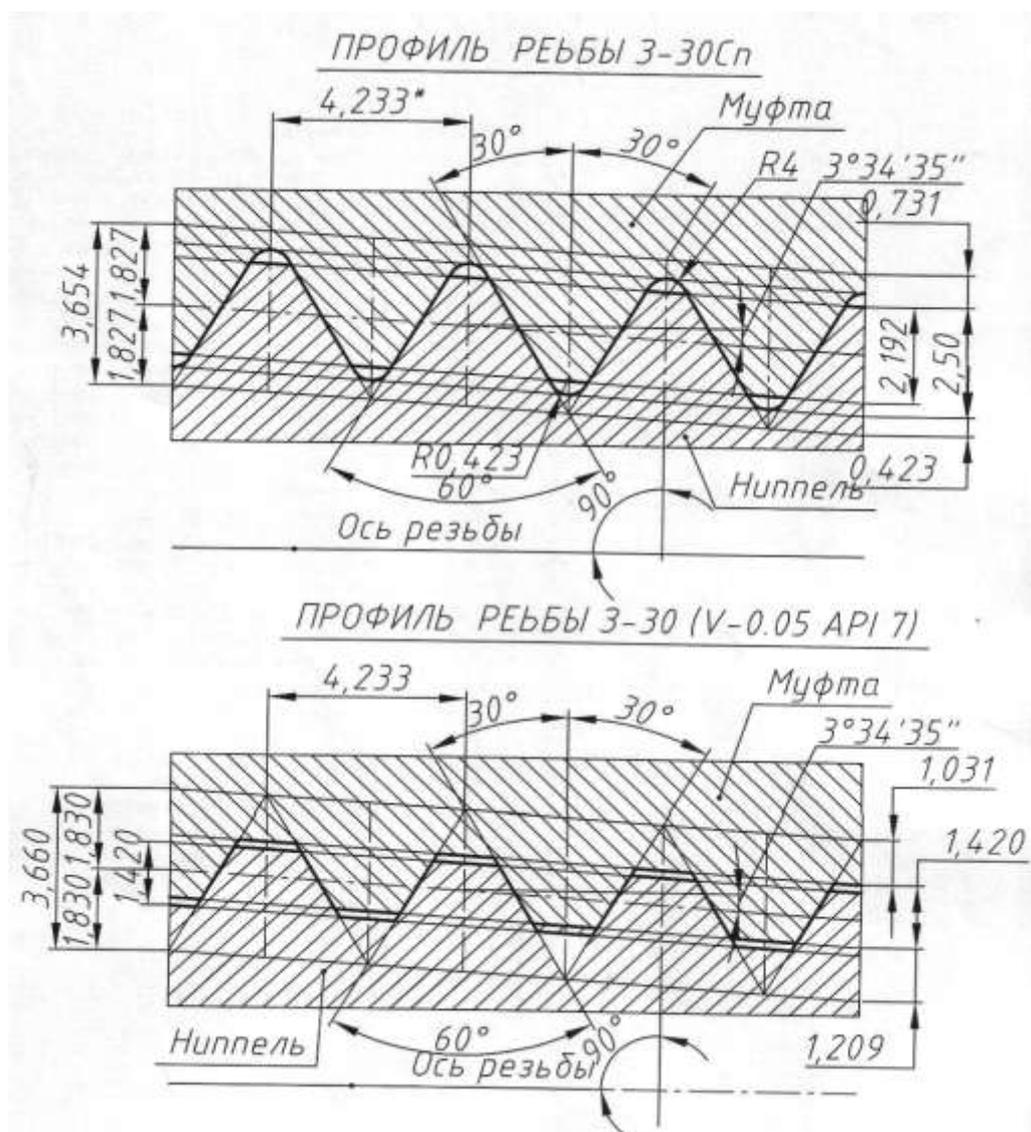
Типы замковых резьб для штанг малого диаметра
